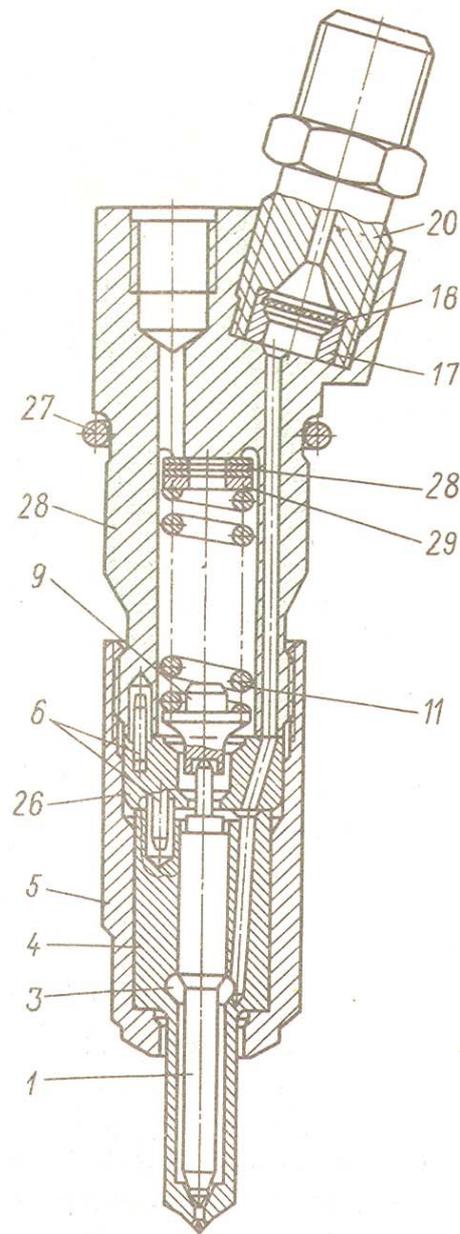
Закрытая форсунка: 1 – игла распылителя;
